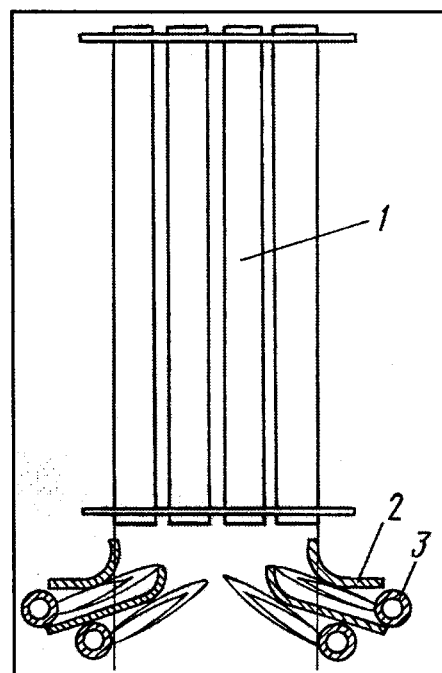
Схема нагрева сердцевин трубчатыми горелками, установленными вне зоны прохождения сердцевин:
